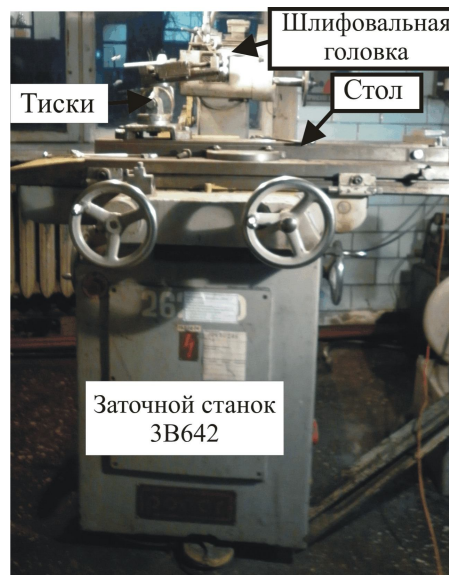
Общий вид заточного станка ЗВ642
